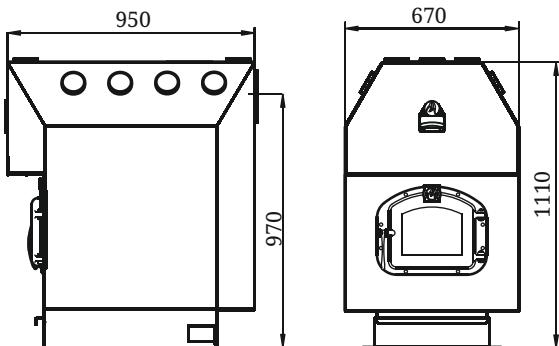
Габаритные размеры печи «Профессор» с выходом трубы назад
